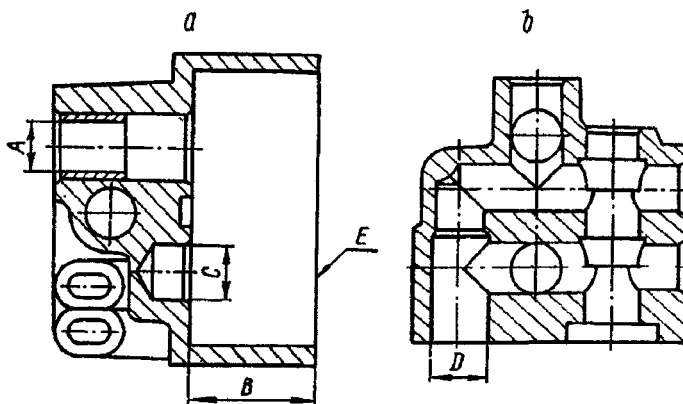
Корпус нагнетающей секции масляного насоса: а — разрез по отверстию под ось зубчатых колес; б — разрез по отверстию под предохранительный клапан
